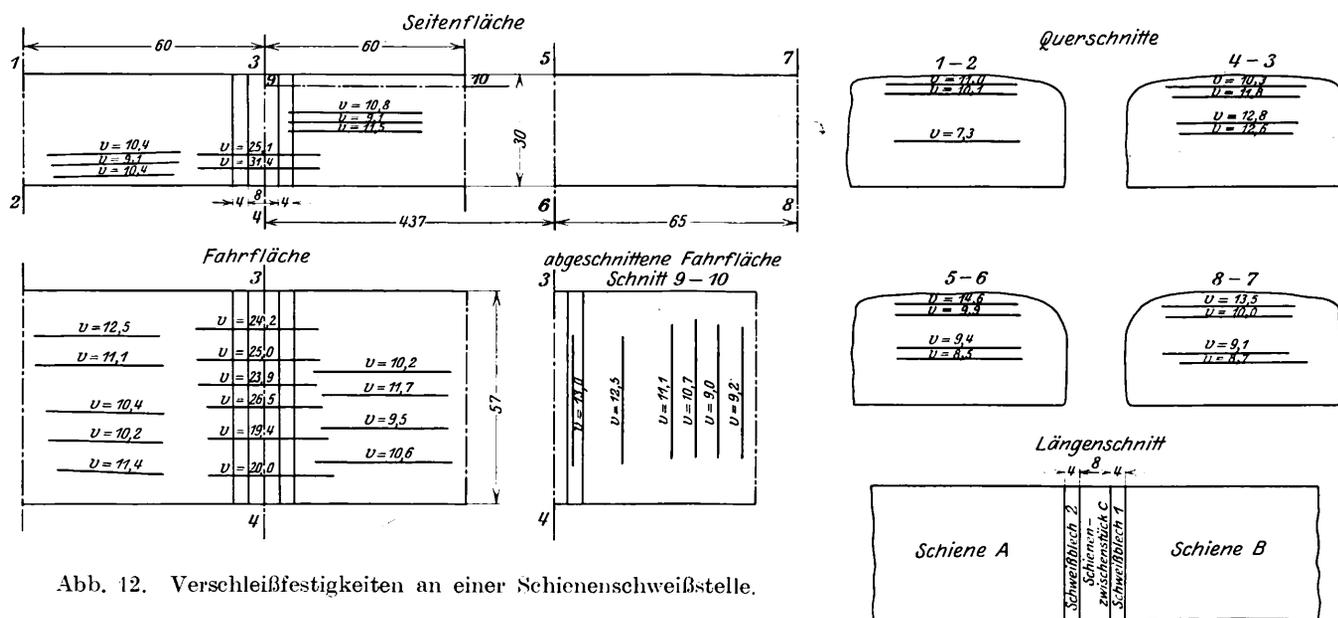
Verschleißfestigkeiten an einer Schienenschweißstelle.
